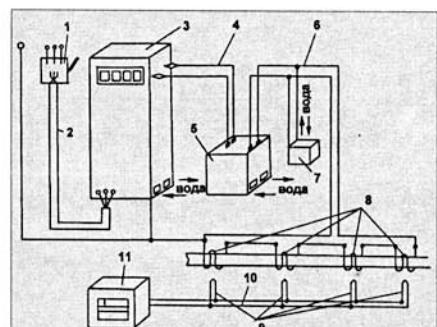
Принципиальная схема установки с инвертором ППЧ-100-2,4 фирмы «Курай» (Уфа) для местной термообработки сварных соединений трубопроводов токами средней частоты: 1 — электрический рубильник; 2 — силовой кабель для питания установки; 3 — тиристорный преобразователь ППЧ-100-2,4; 4 — силовой кабель; 5 — высокочастотный трансформатор Т34-800; 6 — сварочный кабель сечением 140 мм; 7 — конденсатор ЭЗВК-0,5-2,4; 8 — гибкие индукторы из оголенного медного провода сечением 95 мм²; 9 — термоэлектрические преобразователи; 10 — термоэлектродный провод; 11 — автоматический регистрирующий потенциометр
